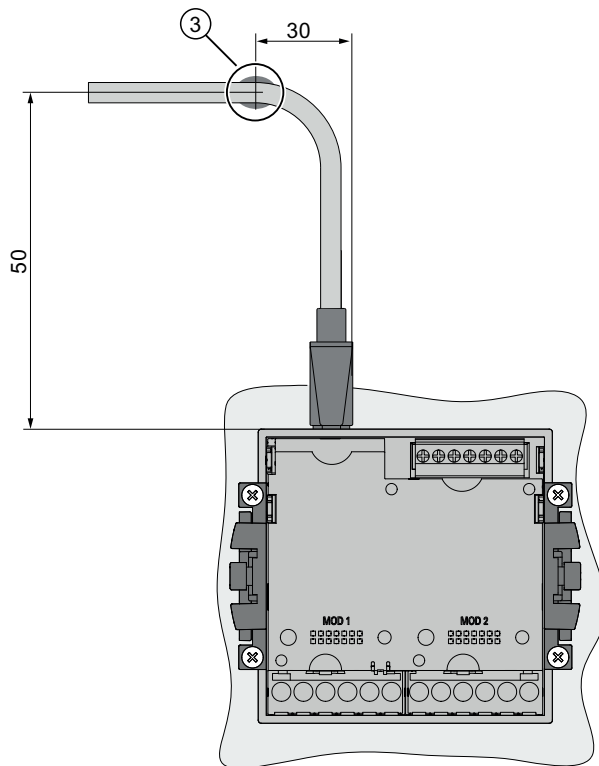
Montageschritt E, Zugentlastung für RJ45-Stecker
